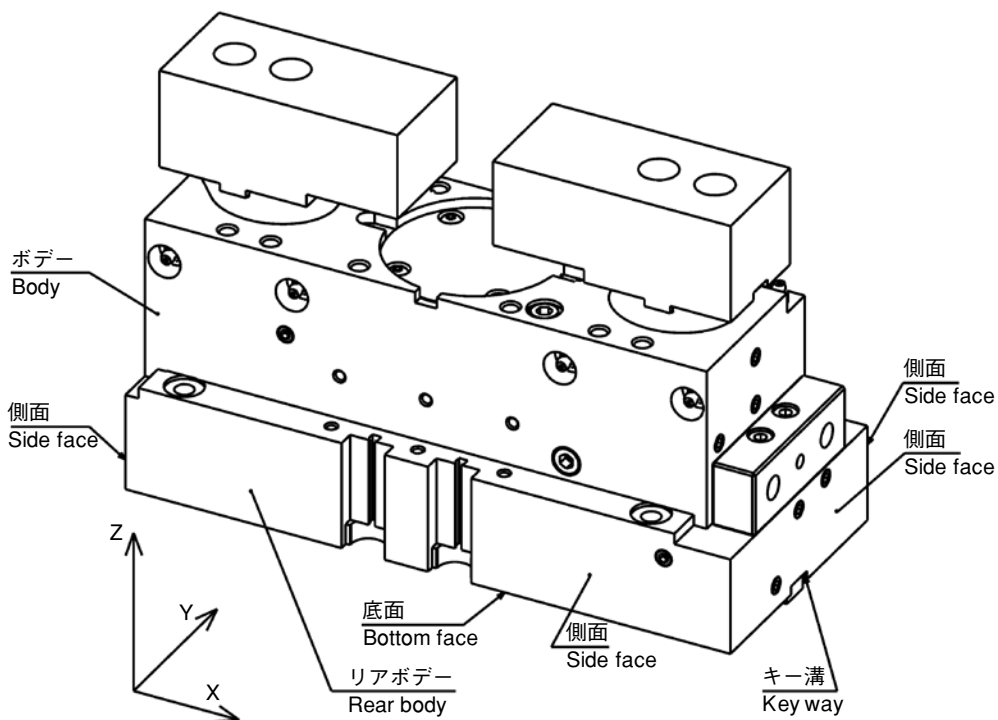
治具モジュールの位置決め Positioning of Jig Module
